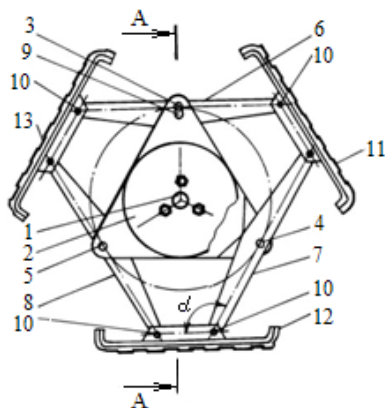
Рушій (вид збоку): *1* – ведучий вал; *2* – маточина;
